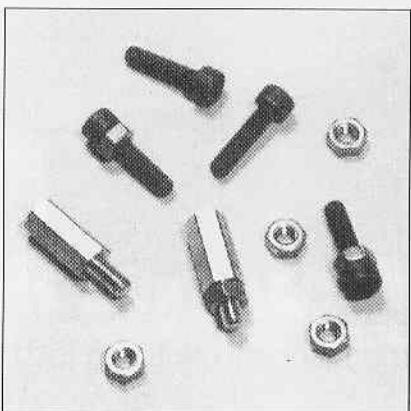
Bei vier Inbusschrauben und zwei Abstandsbolzen wird die Gewindelänge durch eine Mutter verkürzt.
